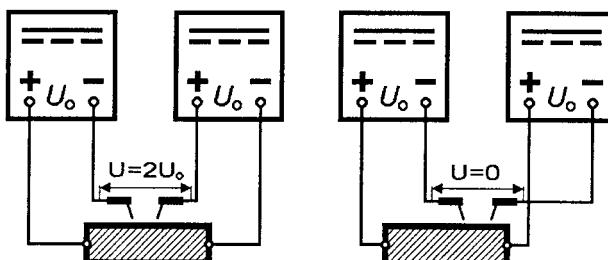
Die zum Schweißen gewählte Polung ist schweißtechnisch bedingt.
